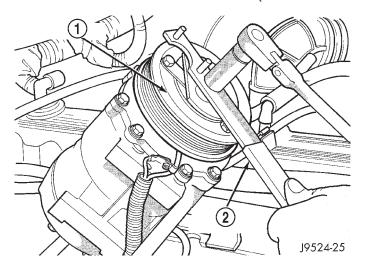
DESMONTAJE DE TUERCA DEL EMBRAGUE - característico
